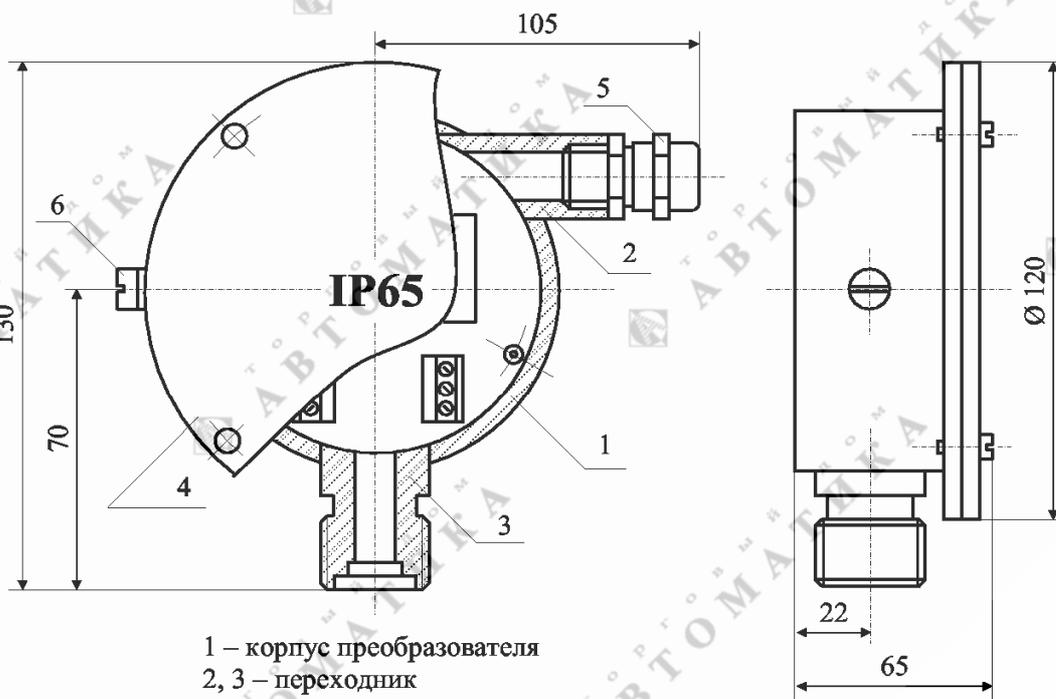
Корпус ПИП прибора рН-4110.ДП.Х.Х
